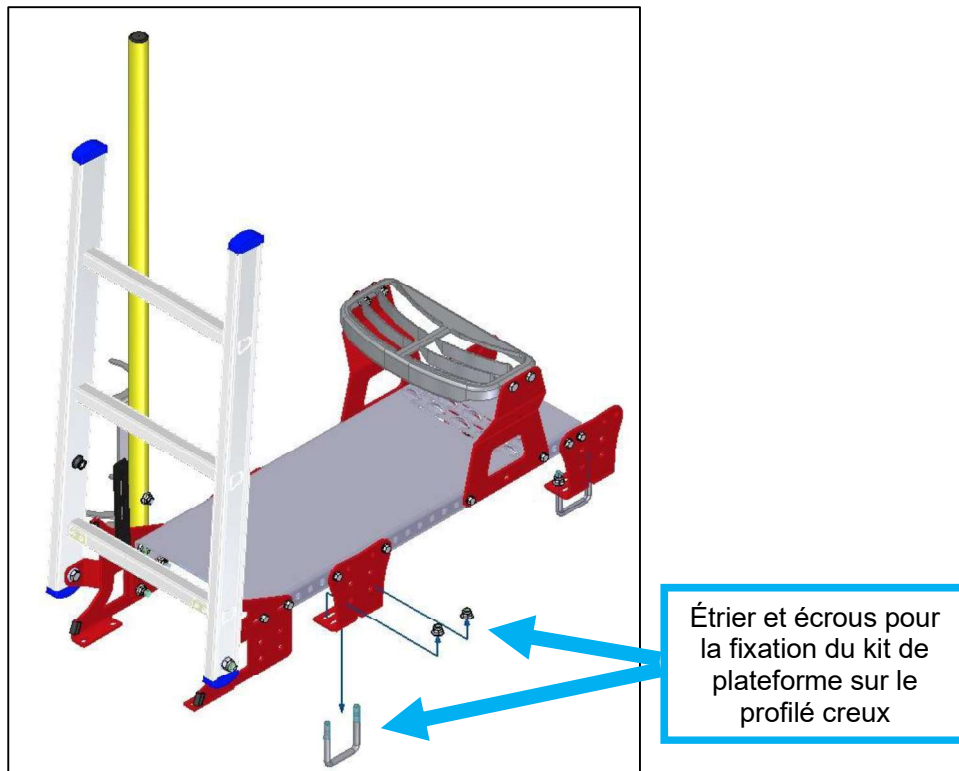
composants du kit de plateforme VS600-1200 sans roue de jauge à l'arrière
